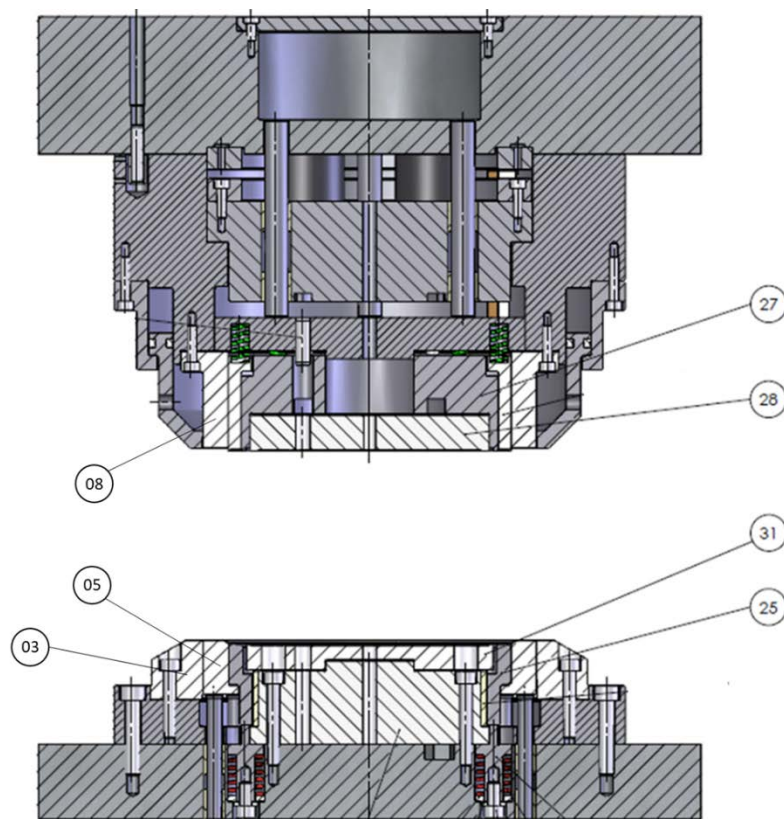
Desenho de conjunto da ferramenta de estampagem
